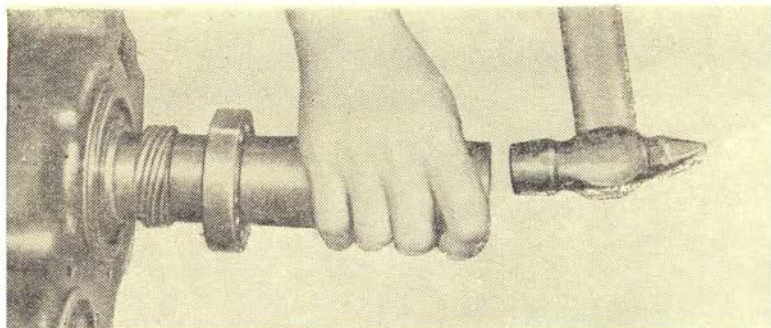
Запрессовка заднего подшипника на ведомый вал
